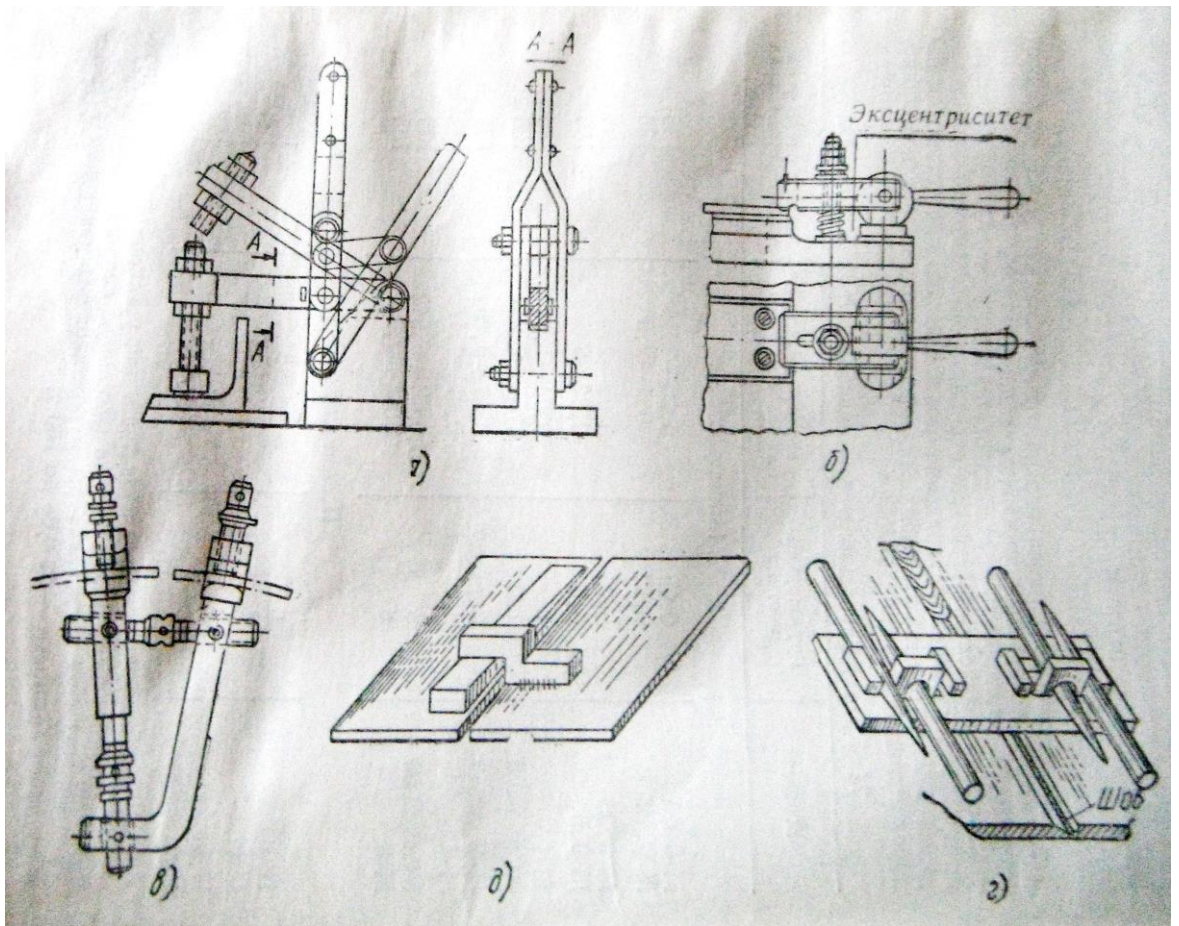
Переносные приспособления для сборочно-сварочных работ.
